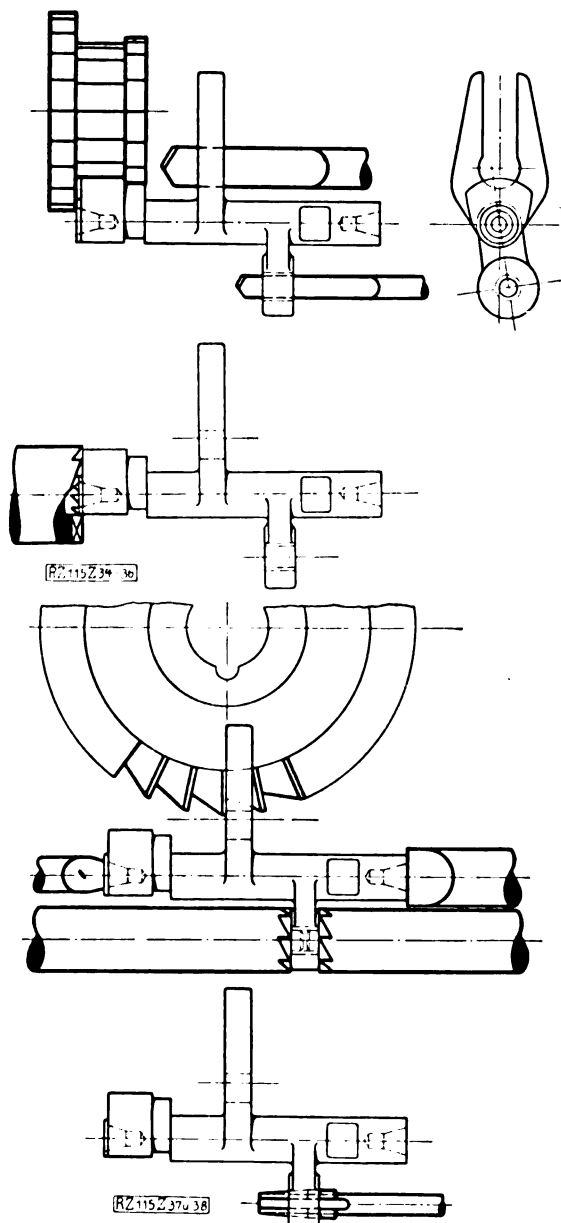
bis 38. Bearbeitung des Exzenterstücks von Nähmaschinen auf der Sondermaschine, Abb. 39 und 40.
